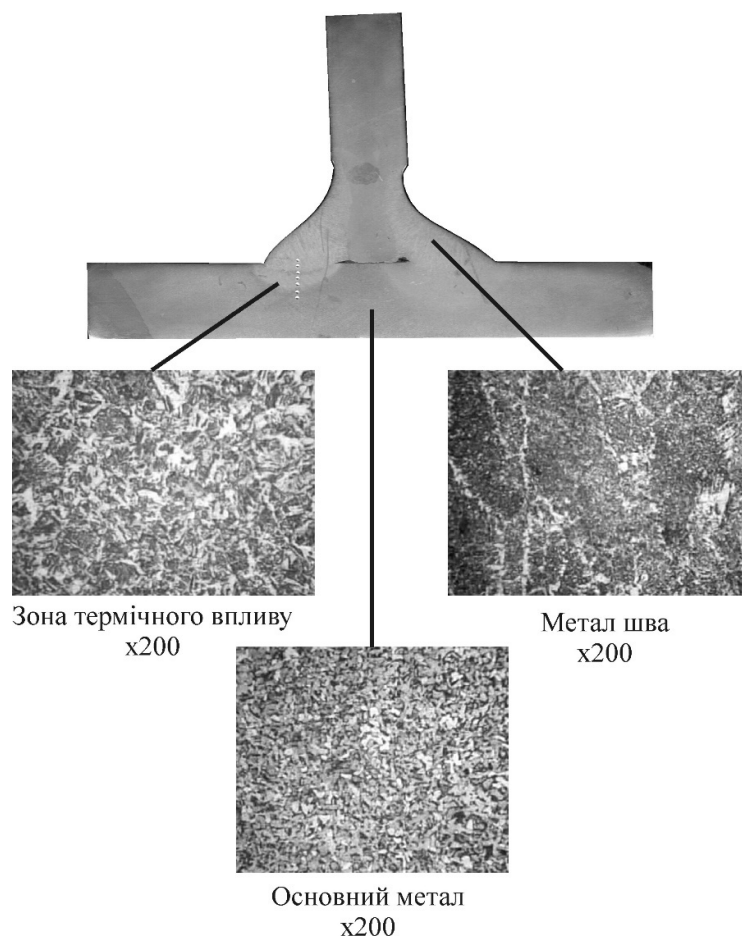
Макро- та мікроструктура зварного з'єднання ТЗ
